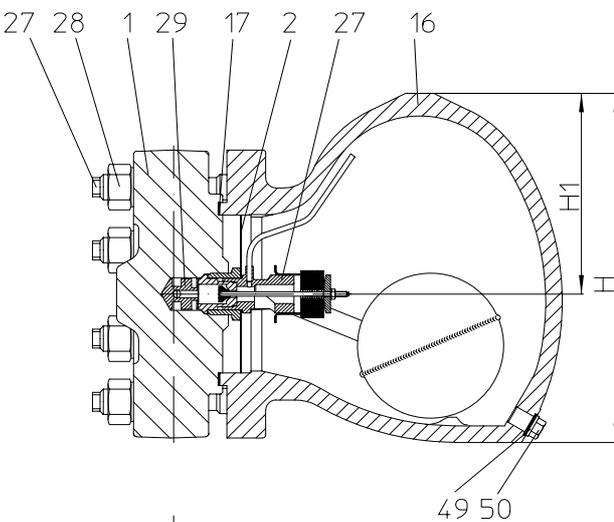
3 / 632...3 mit Schweißmuffen
